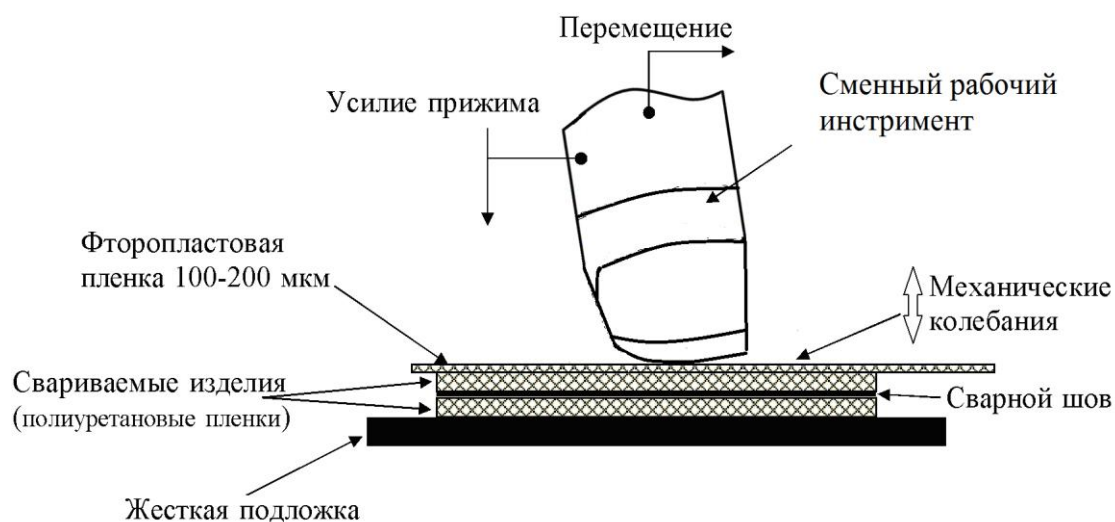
Схема ультразвуковой сварки без обрезки
